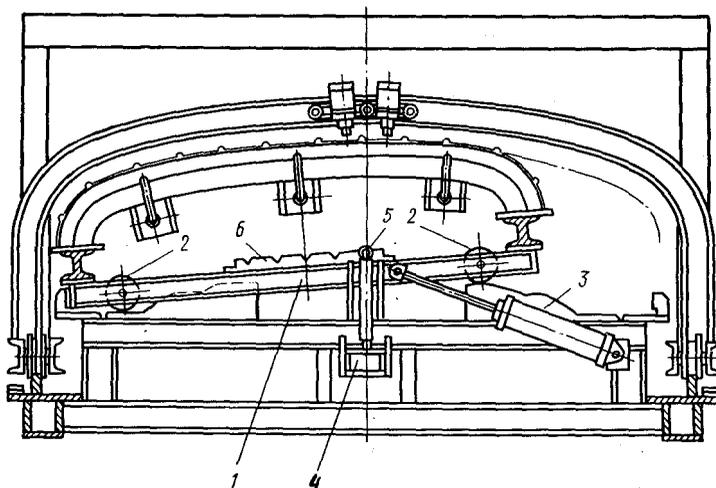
Универсальный стэнд для сварки секций крыши
